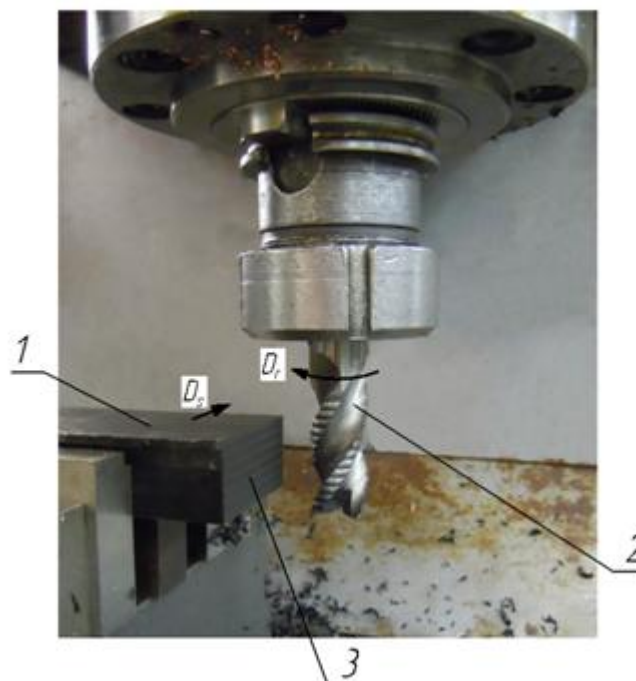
Схема фрезерования плоскости: 1 – заготовка; 2 – фреза; 3 – обработанная поверхность
